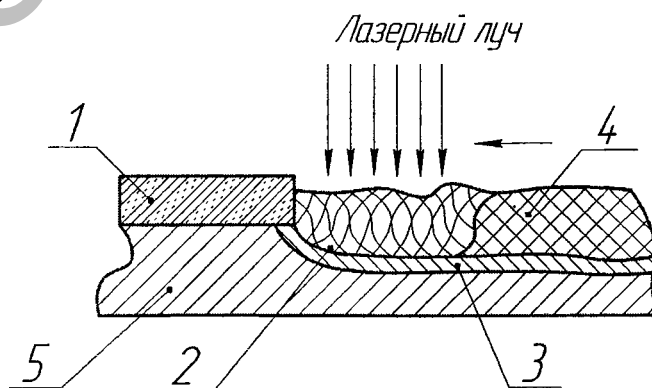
Схема лазерной наплавки: 1-обмазка (материал будущей наплавки); 2-расплав; 3-зона лазерной закалки; 4-наплавленный слой; 5-основной металл
